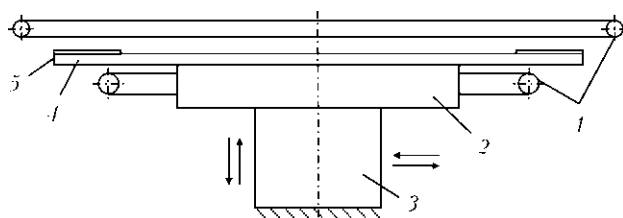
Схема индукционной наплавки тонких плоских деталей с приложением вибрации в процессе наплавки: 1 — индуктор; 2 — стол; 3 — вибратор (стрелками показано направление приложения колебаний); 4 — деталь; 5 — порошкообразный твердый сплав
